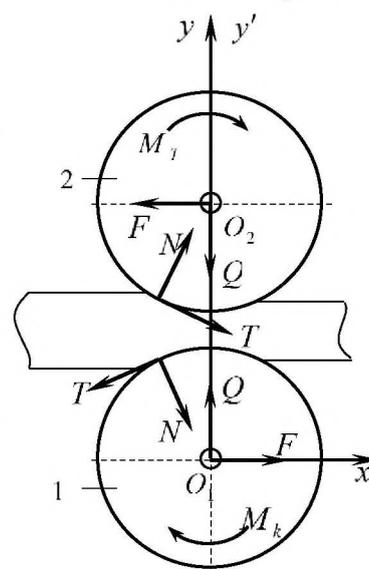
Схема валковой пары без межвалкового передаточного механизма:
